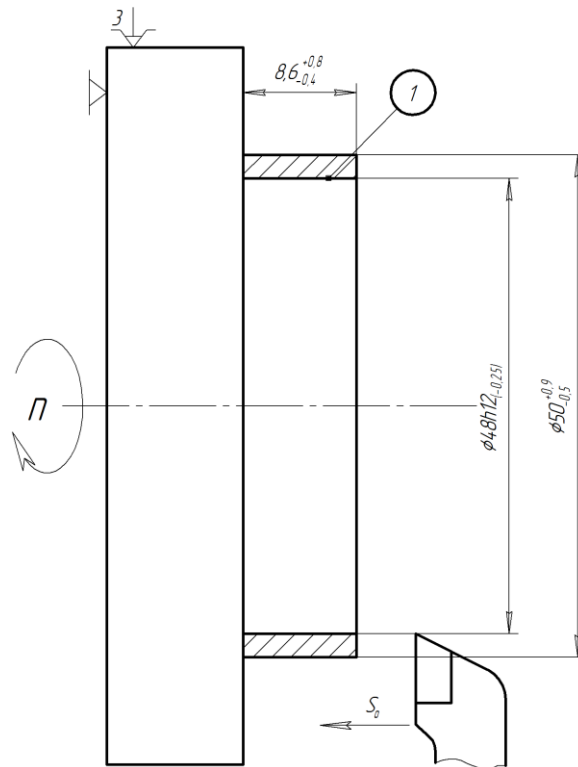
Схема обробки поверхні Ø48h12
